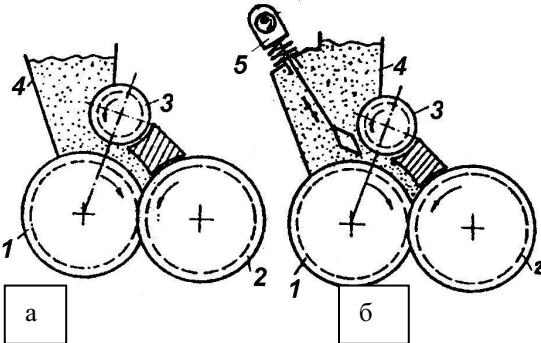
Схемы конструкций усовершенствованного валкового пресса: 1, 2 – рабочие валки; 3 – дополнительный валок; 4 – загрузочная воронка; 5 – виброуплотнитель.
